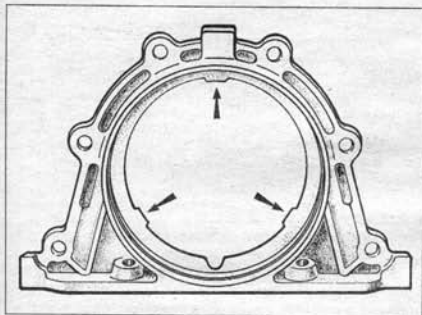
Держатель заднего сальника коленчатого вала. Стрелками показаны выступы для центрирования держателя относительно фланца коленчатого вала
